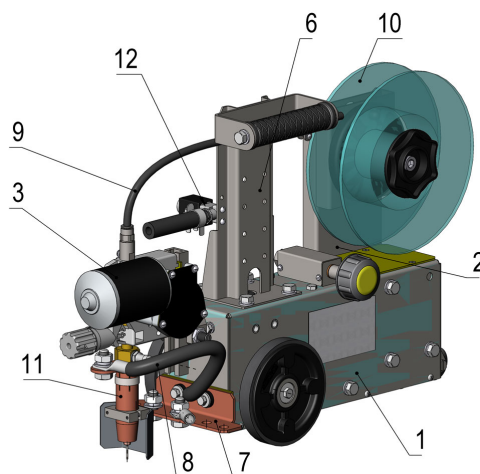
Основные части трактора (сварка в среде защитного газа)
